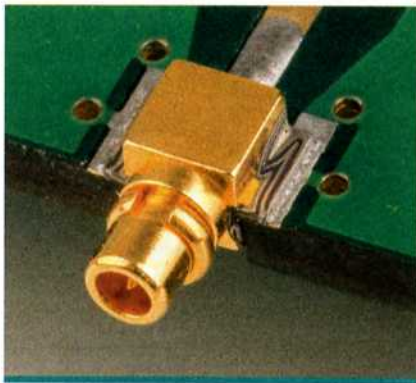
MMCX-Edge-Mount Steckverbinder in SMT auf die Leiterplatte gelötet.
